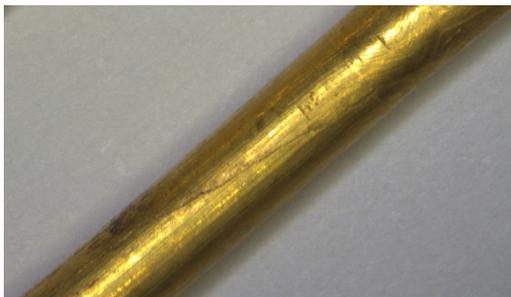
Rezept 4: Ziehvorgang: mit Goldblech (940/- Au) ummantelter Silberrostab, Detail: Fuge. – Recipe 4: drawing process, gold-coated (940/- Au) silverwire, detail: joint.
